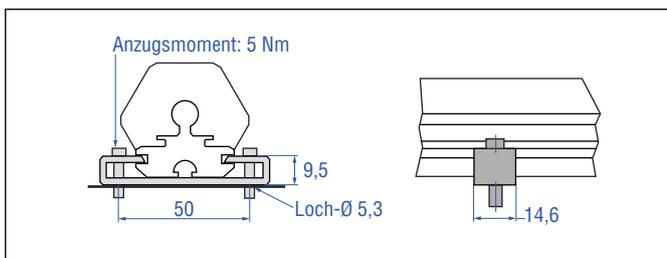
Montageklammern (Artikelnr. 400 802) mit Zylinderschraube M5×20
